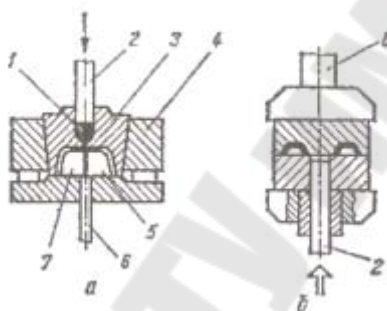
Схемы литьевого прессования пластмассовых изделий:
